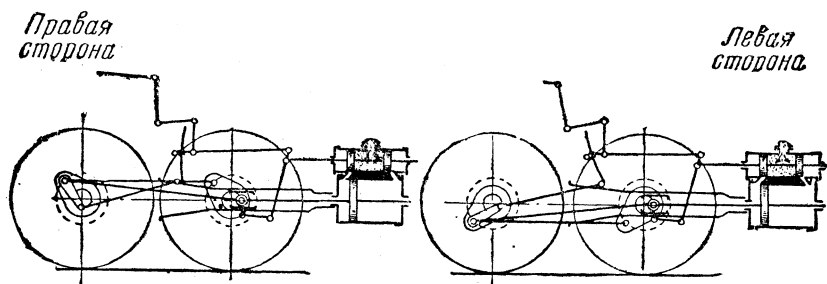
Проверка укрепления поршневого диска на штоке, соединения штока с кресткопфом и плотности запрессовки пальца и оси ведущего колеса
